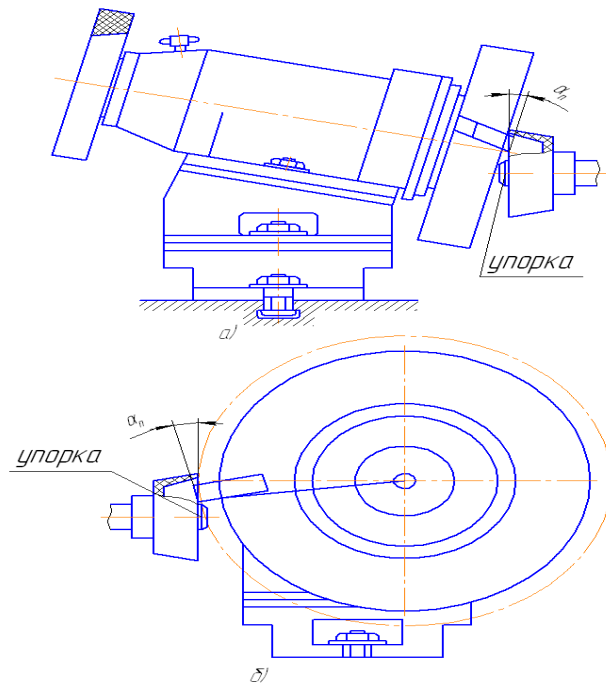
Схема налаштування пристосування для заточування фрез: *a* – по торцю; *б* – про циліндру
